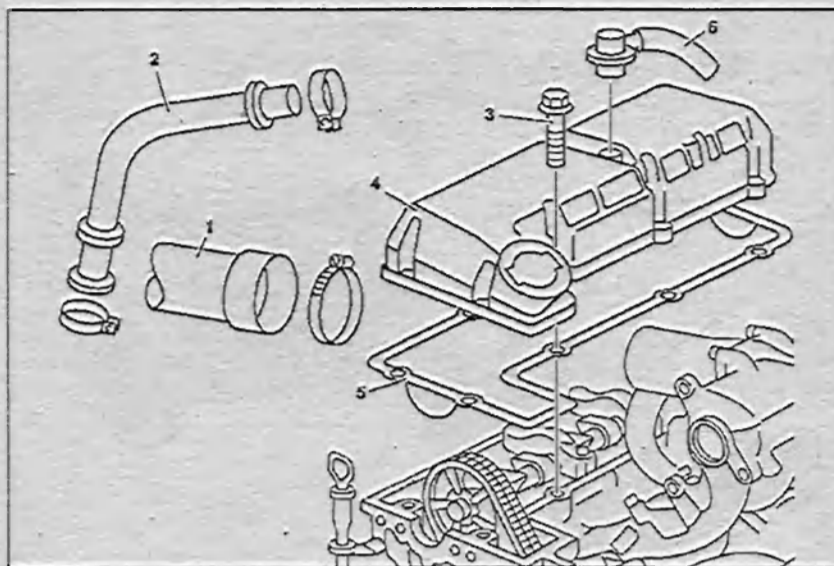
Крышка головки блока цилиндров двигателя 601.943:
